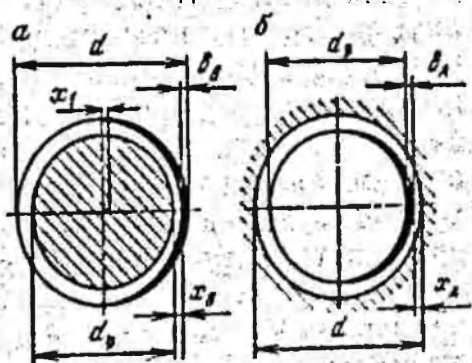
Схемы износа и обработки деталей под ремонтный размер для вала (а) и отверстия (б)
